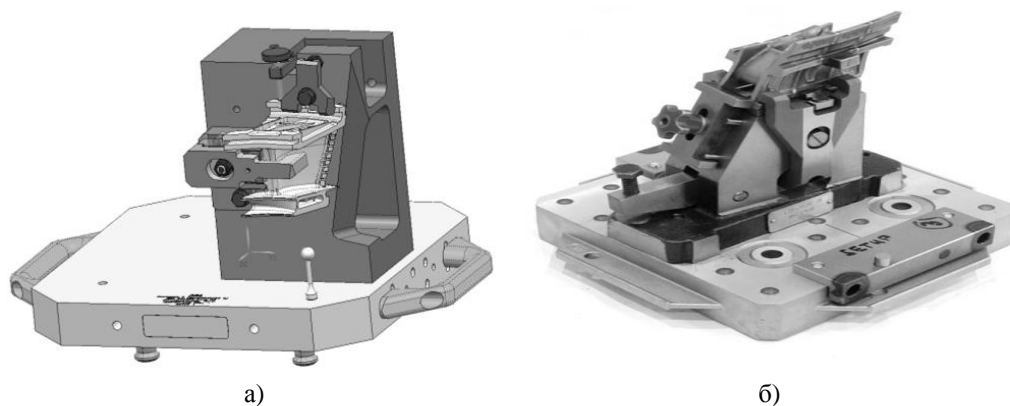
3-D модель – а) и общий вид – б) станочного поворотного приспособления для установки, разворота и обработки базовых установочных поверхностей сопловых лопаток методом глубинного шлифования на станке фирмы «Mägerle AG» MFP-050.65.65
